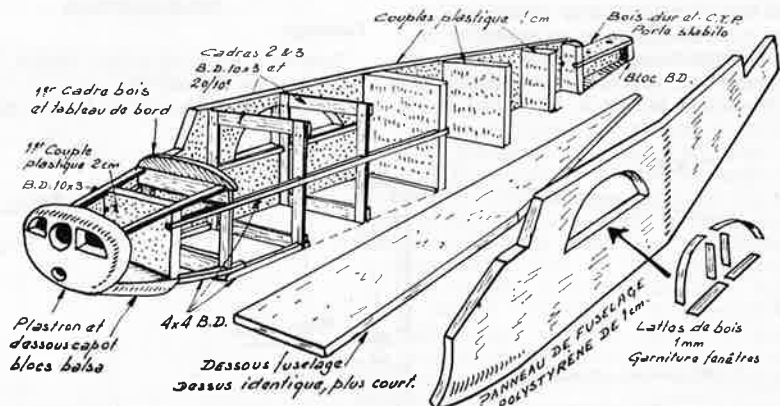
CONSTRUCTION DU PILATUS PORTER (1959)
